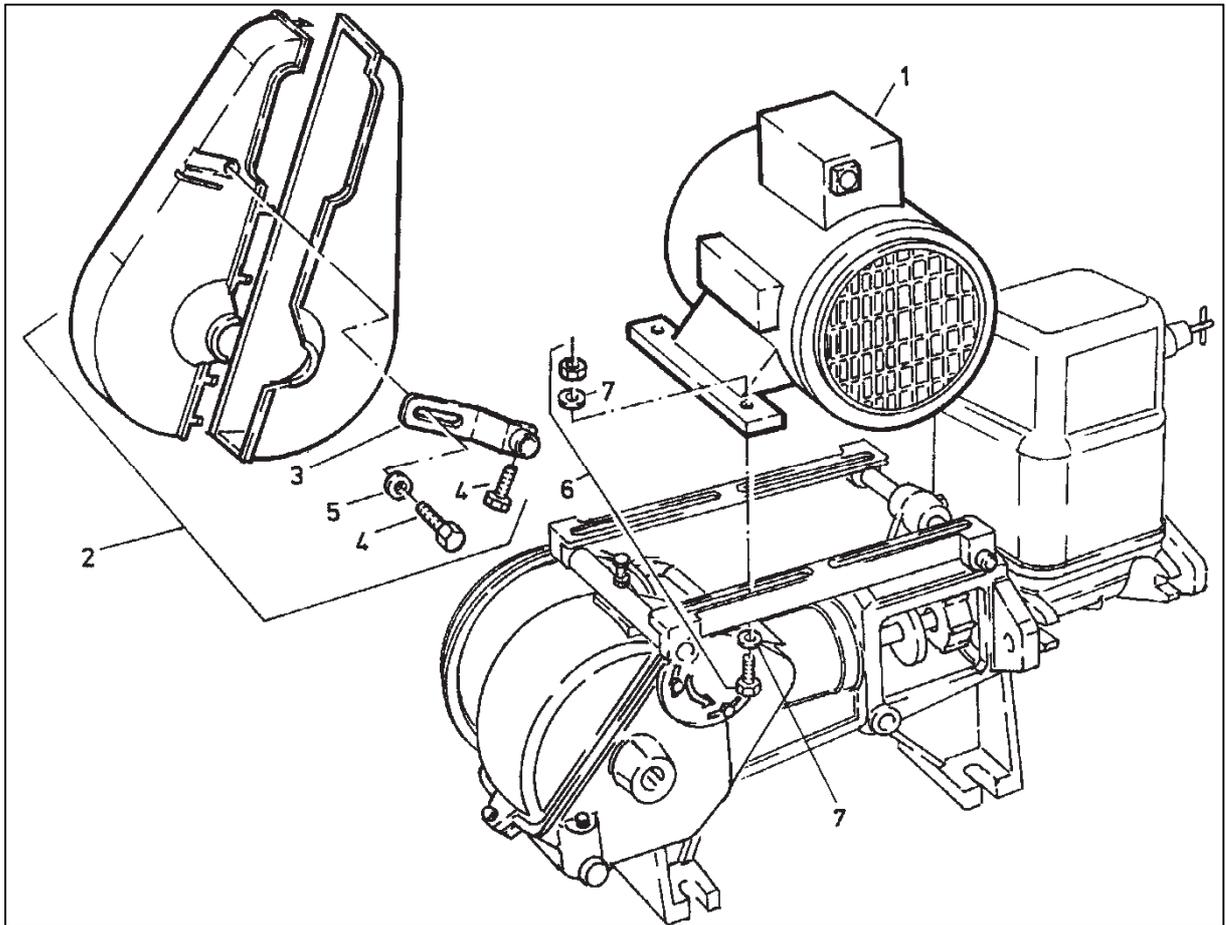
Explosionszeichnung Motoraufbau LG 100-400
